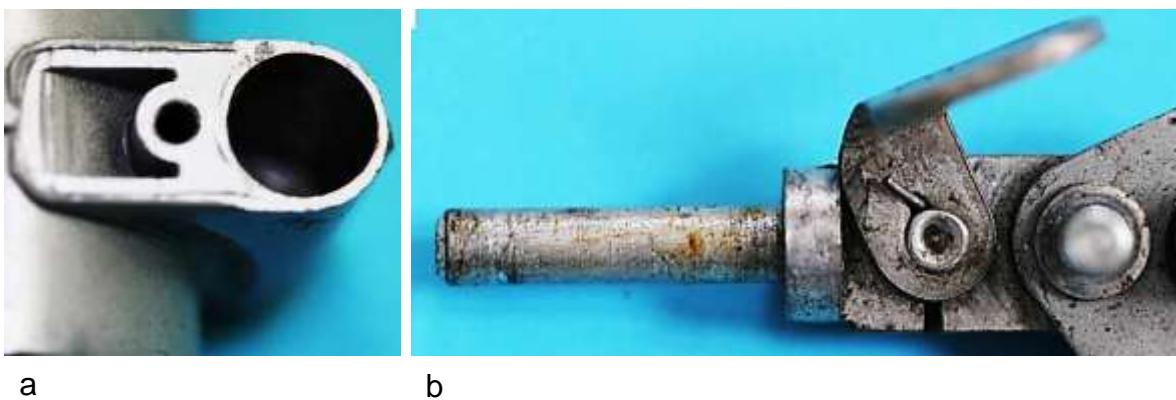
Kippvorrichtung: a) Zylindrischer Hohlraum, b) Drehbolzen mit Fußpedal
